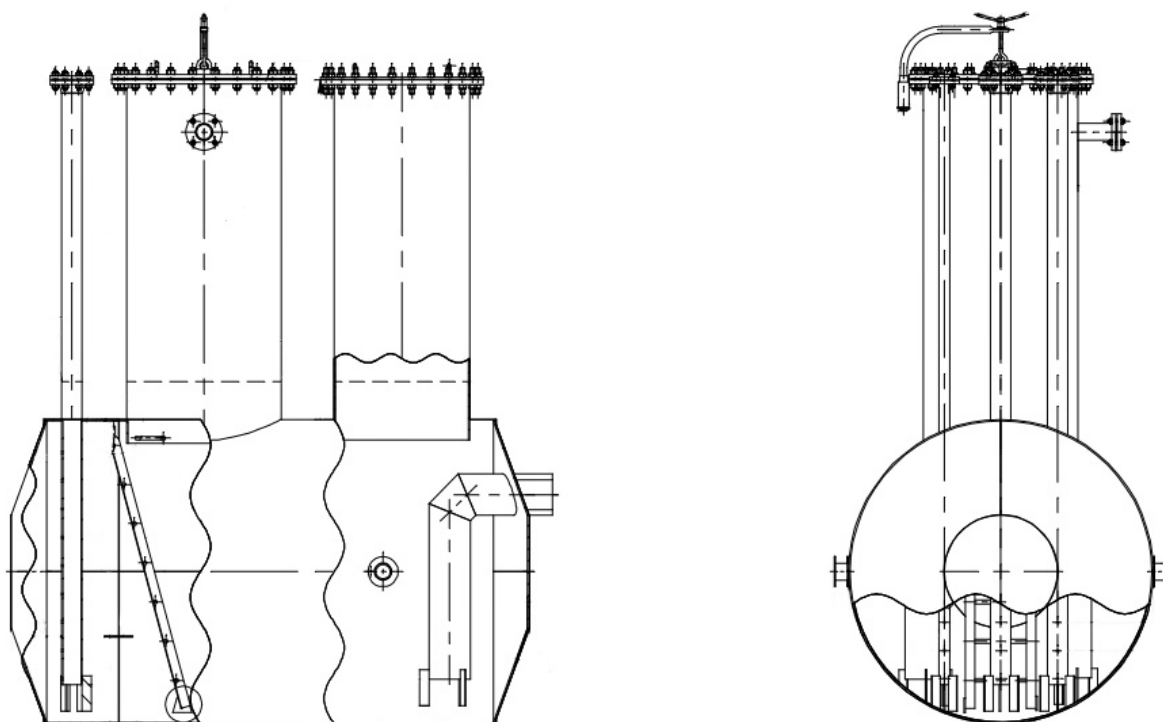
Эскиз общего вида резервуаров РГС-5
